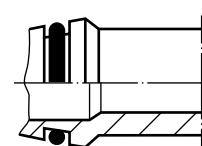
Резьбовой штуцер с конической уплотнительной поверхностью 24°: форма В для шлангового соединения
